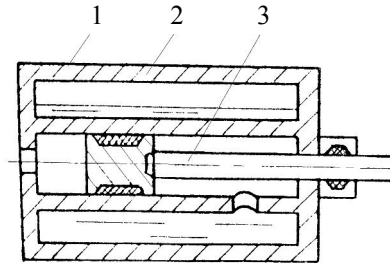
Схема двоциліндрового пневматичного накатника:
